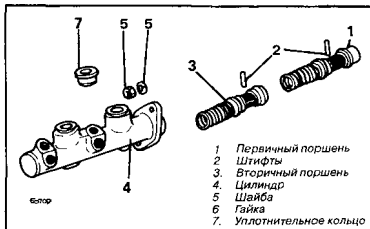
27 Детали главного тормозного цилиндра Bendix
